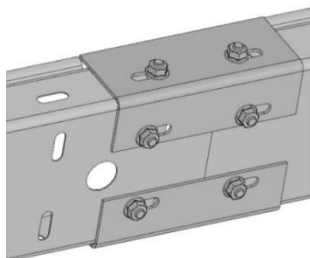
Соединение лотков с помощью соединителя бокового с дополнительным нижним креплением заземляющей
